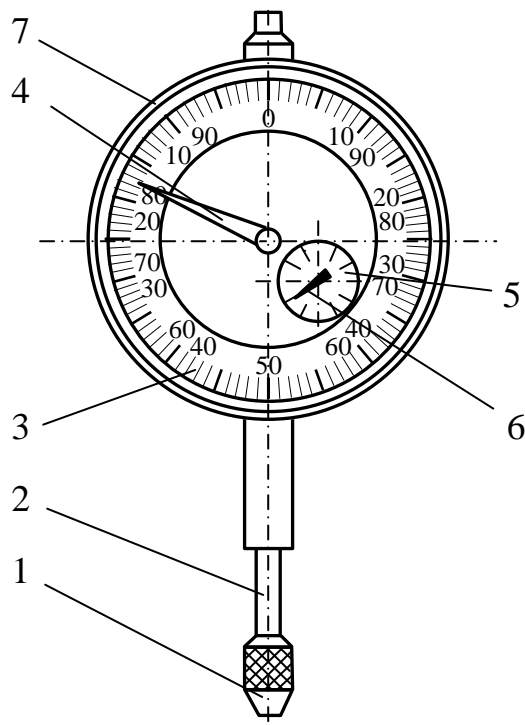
Внешнее строение индикаторной головки: 1 – измерительный наконечник; 2 – измерительный стержень; 3 – основная шкала; 4 – большая стрелка; 5 – шкала; 6 – маленькая стрелка; 7 – ободок
